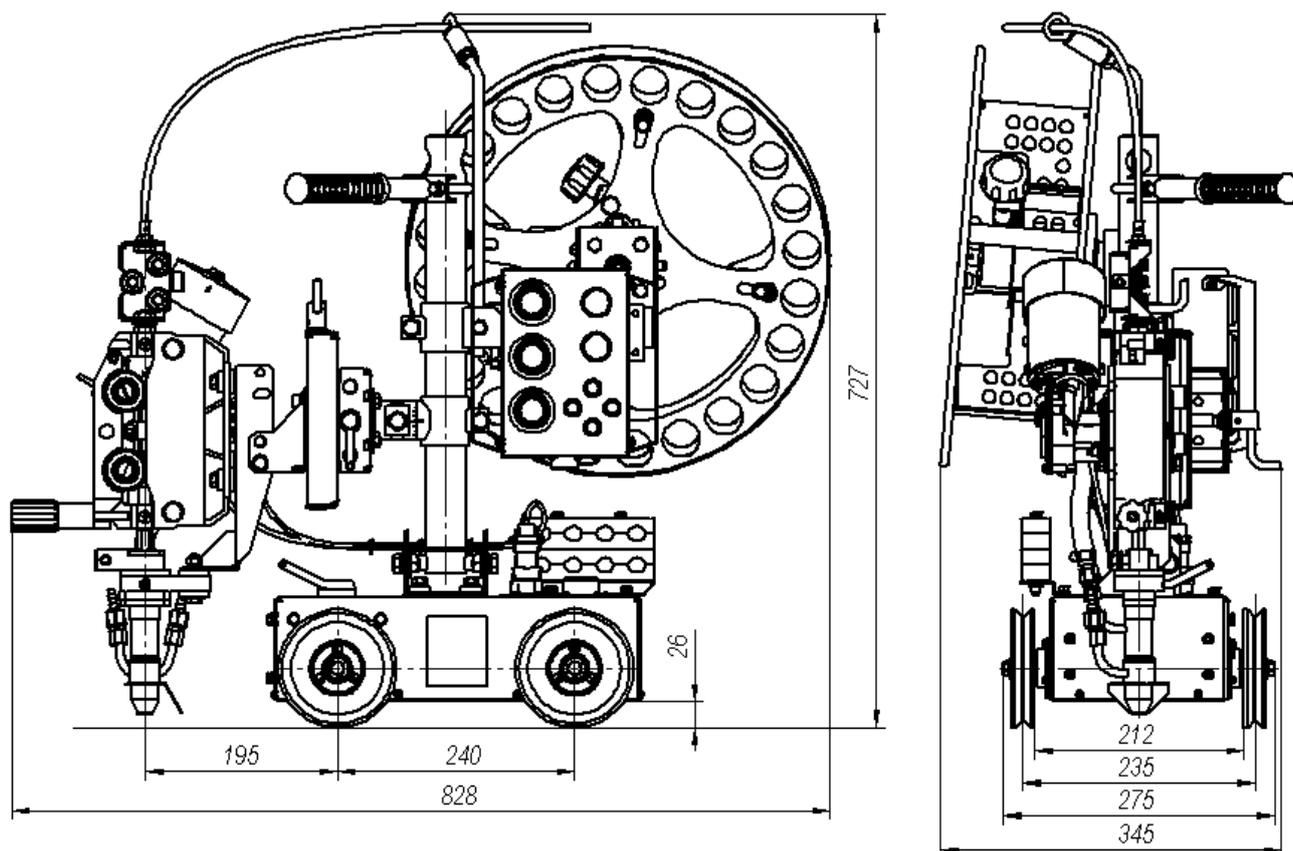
Автомат сварочный АДГ-630. Общий вид.
